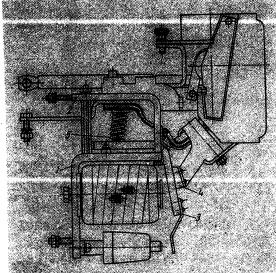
Конструкция контакторов серии КП 500 с НЗ главными контактами. 1 — главный контакт; 2 — изоляция; 3 — якорь; 4 — контактная камера; 5 — вспомогательная пружина.
